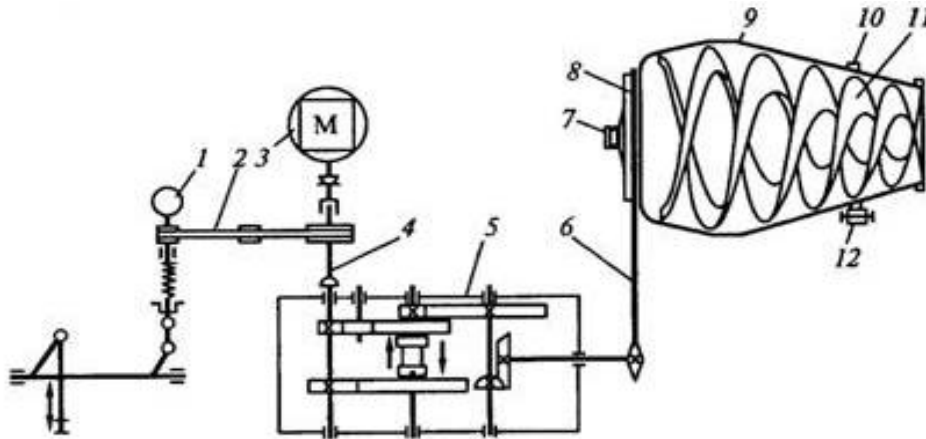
Кінематична схема автобетонозмішувача з механічною передачею (ланцюговою і шестеренчастим редуктором)
